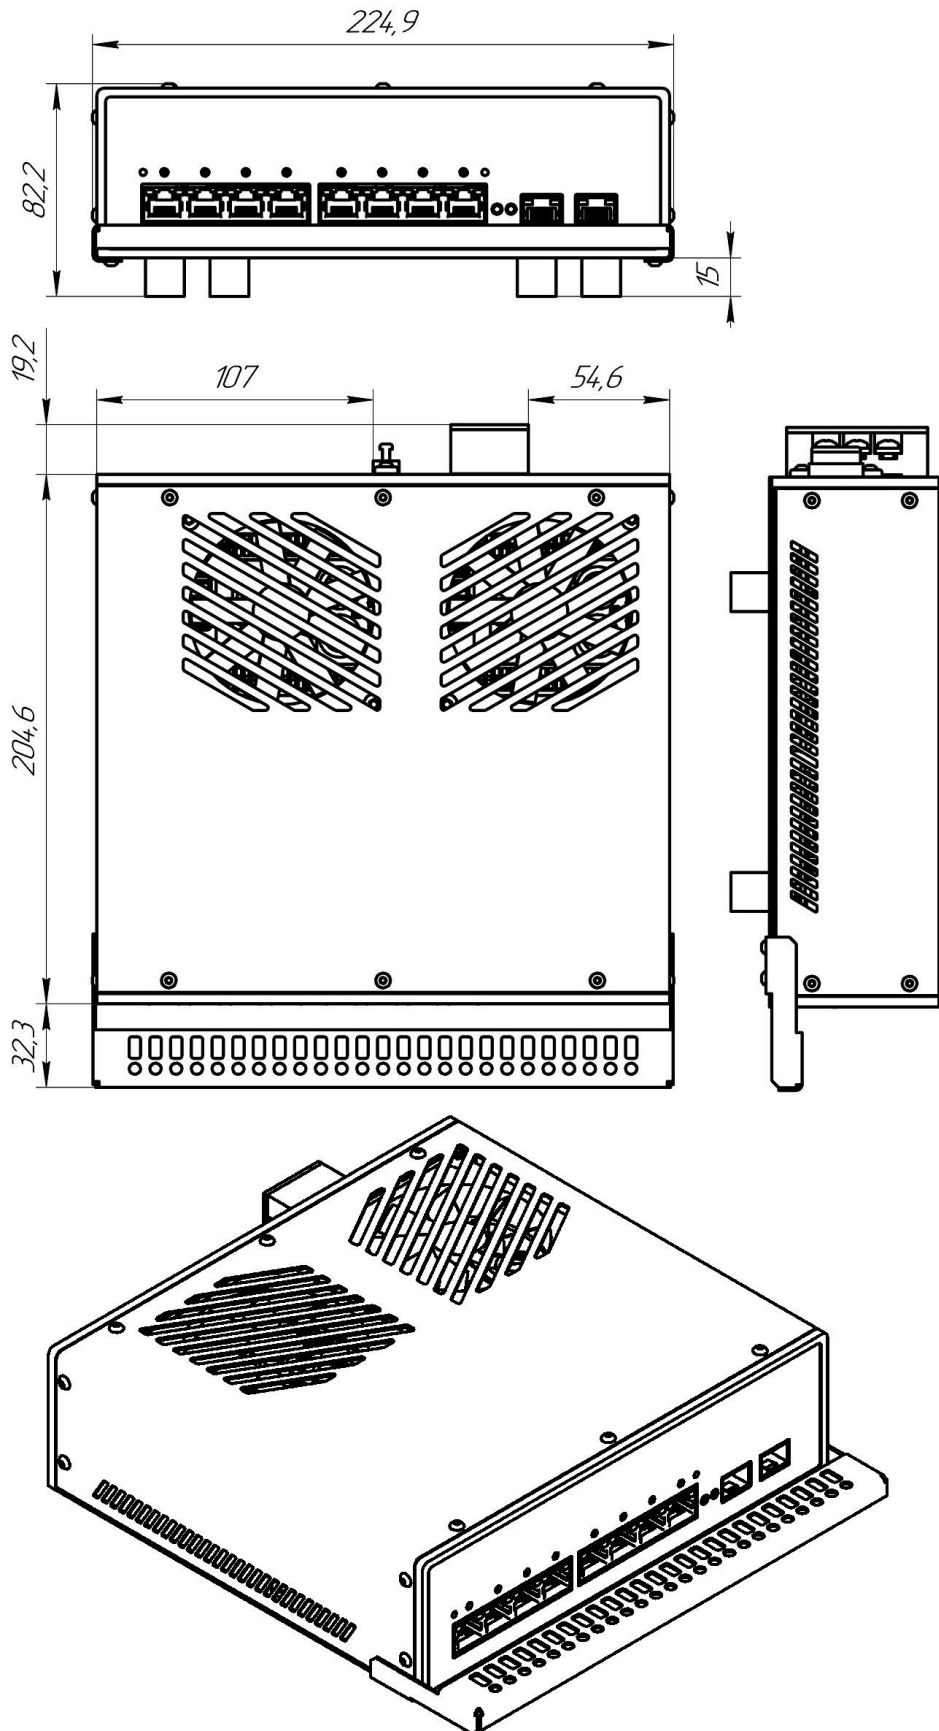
Габаритно присоединительные размеры коммутатора PRO-POE0820W
